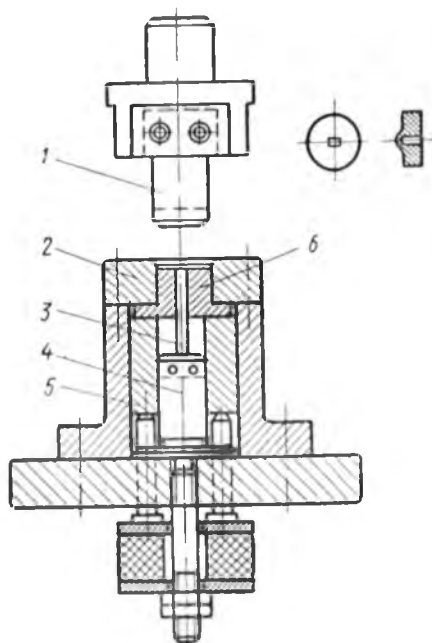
Штамп для прокалывания отверстия в заготовке
